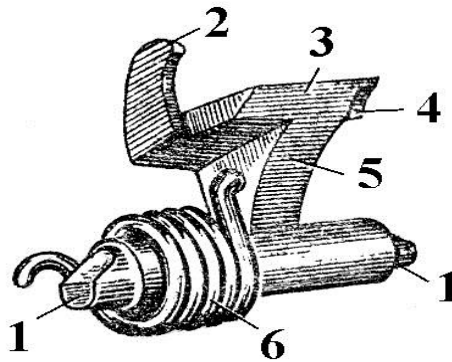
Шептало (1 — цапфы шептала; 2 — зуб; 3 — носик шептала; 4 — выступ; 5 — стойка шептала; 6 — пружина шептала)
